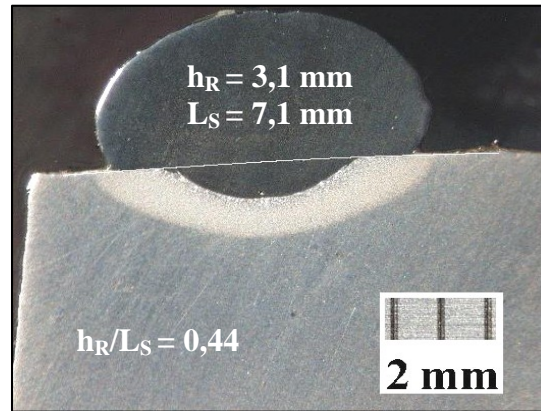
Macrografia de uma solda realizada com corrente de soldagem de 70A e velocidade de soldagem de 8 cm/min. Ataque: Nital 2%.
